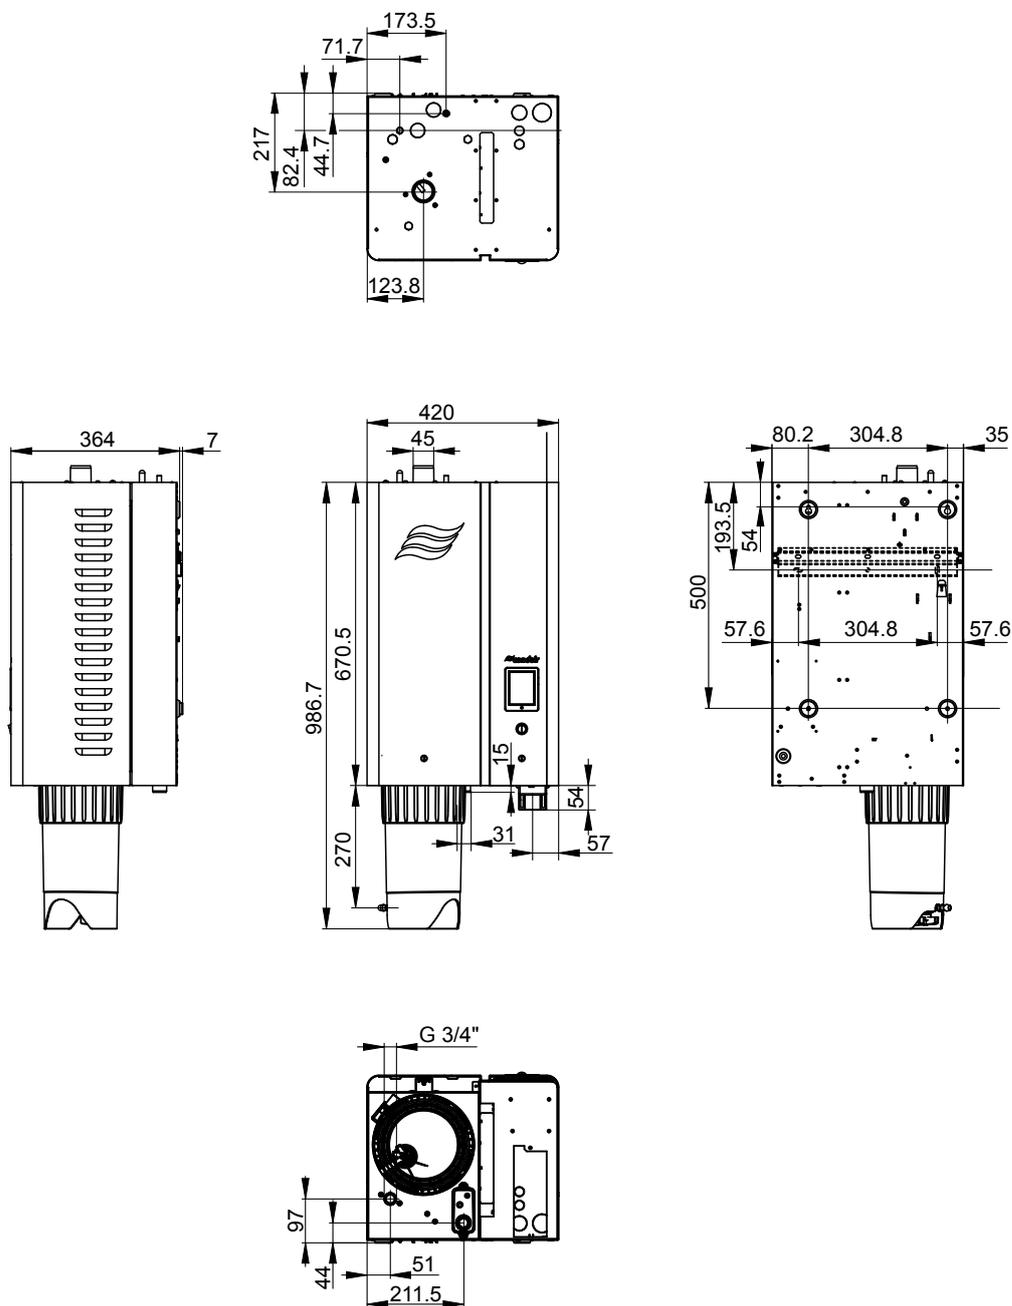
Dimensioni del modulo "S" (misure in mm)
